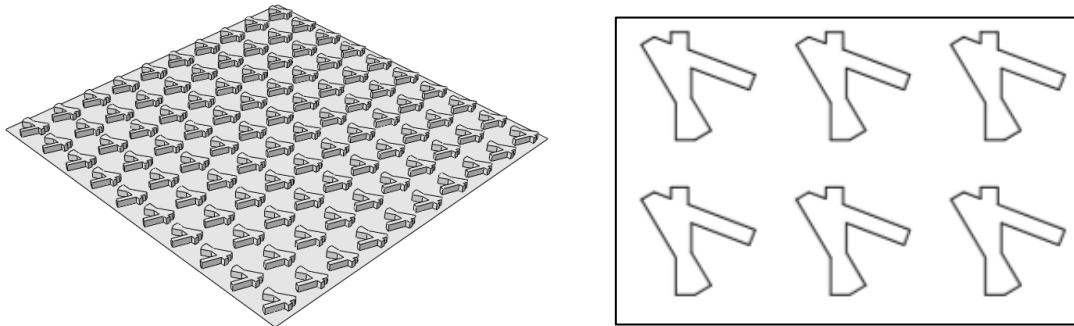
Matriz #3. Vista en perspectiva y en planta.
